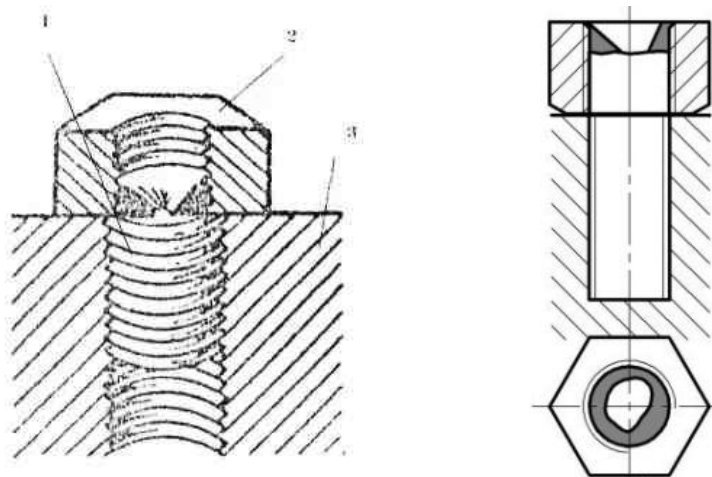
Приварена гайка до шпильки: 1- шпилька; 2- гайка; 3- деталь
